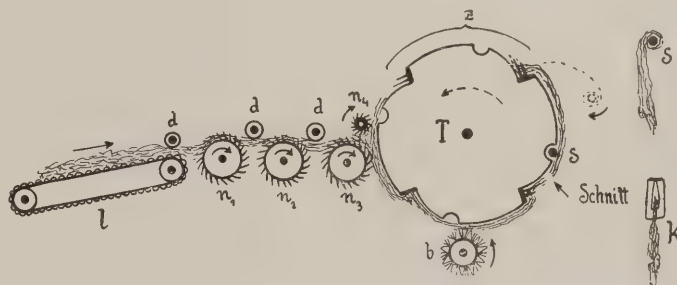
Oeffner, Filling-, Risten- oder Bärtelmaschine. s . . . Bartstab, 1 cm dick, 75 - 80 cm lang für die Rundkämmaschine, k . . . Kluppe oder Buch für die Flachkämmaschine.
